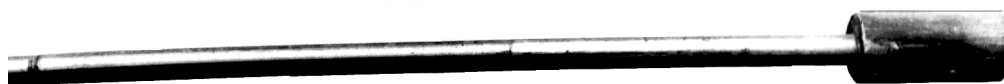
Пруток, полученный методом обратного прессования из сплава Д1 на прессе усилием 500 кН
